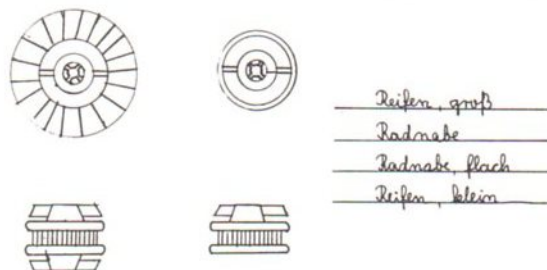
Schautafel mit Skizzen der Bauelemente mit einschiebbaren Kärtchen mit den Namen der Bauelemente.
